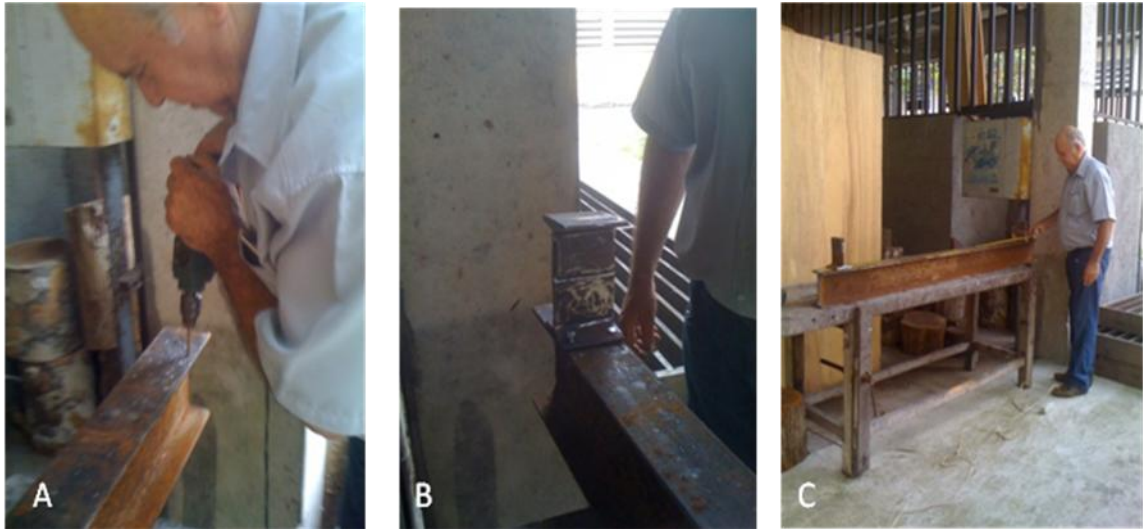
A – Furação do suporte B- Fixação do suporte C – Suporte da viga
